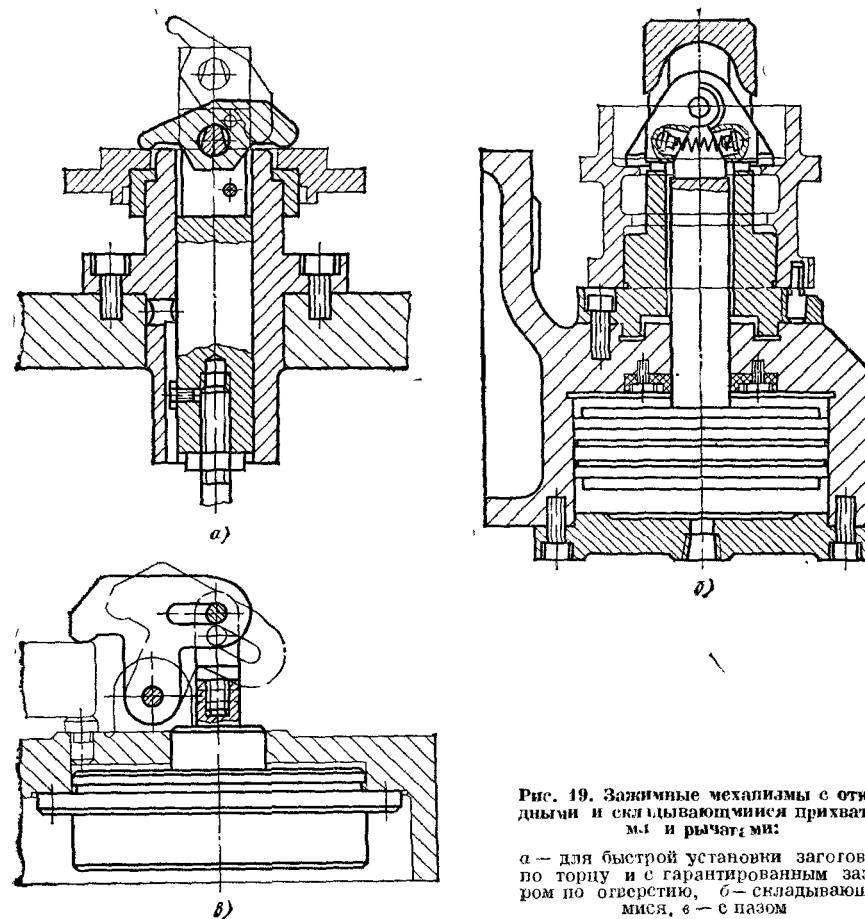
Зажимные механизмы с откидными и складывающимися прихватами и рычагами:
